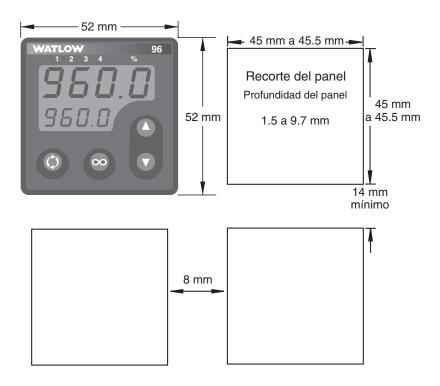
Dimensiones de los recortes de panel del controlador Serie 96.
